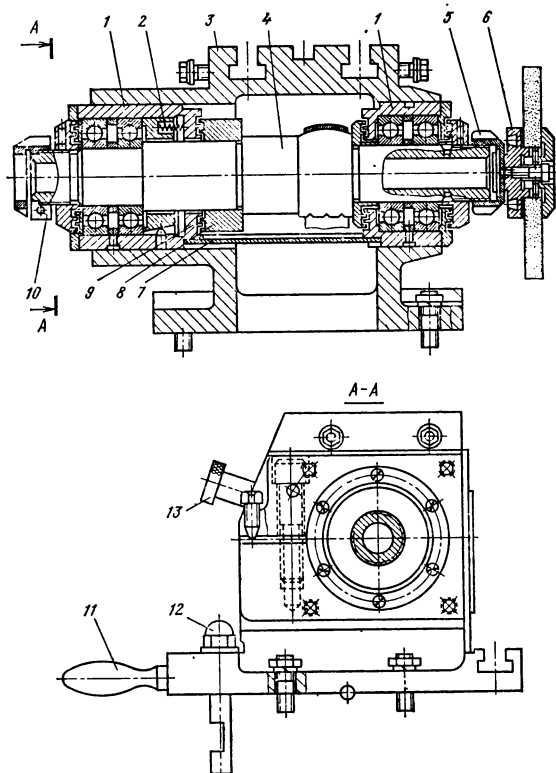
Шлифовальная головка универсально-заточного станка мод. 3В642
